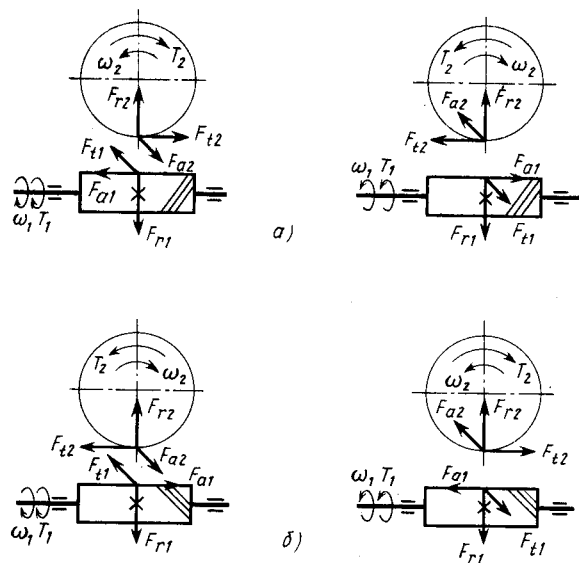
Схема сил в зацеплении червячной передачи:
